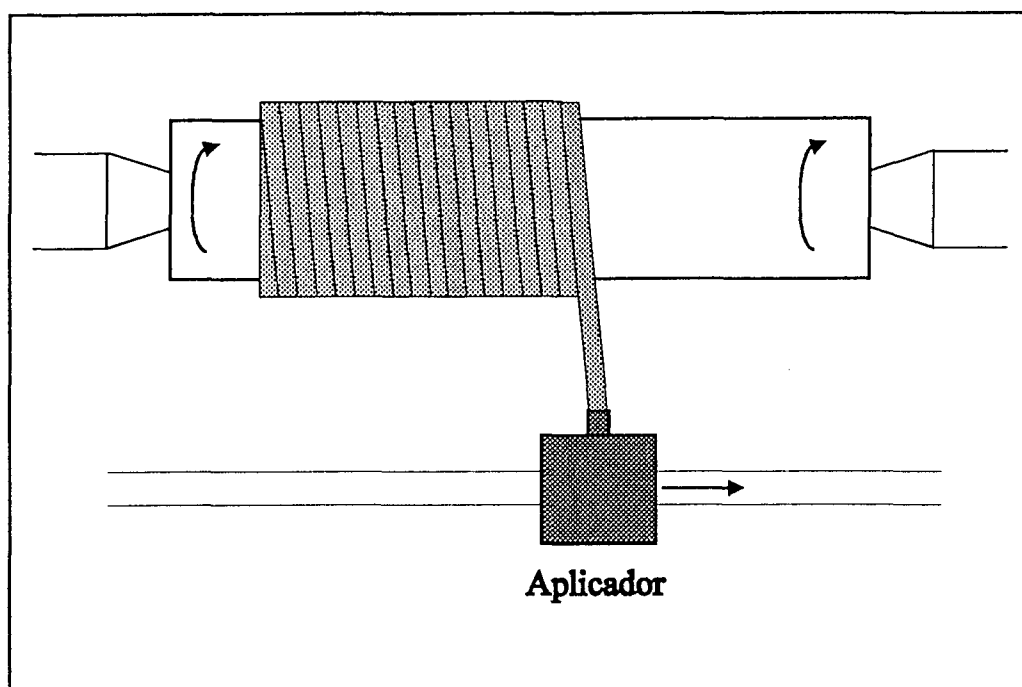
Aplicação da borracha sobre cilindro metálico
